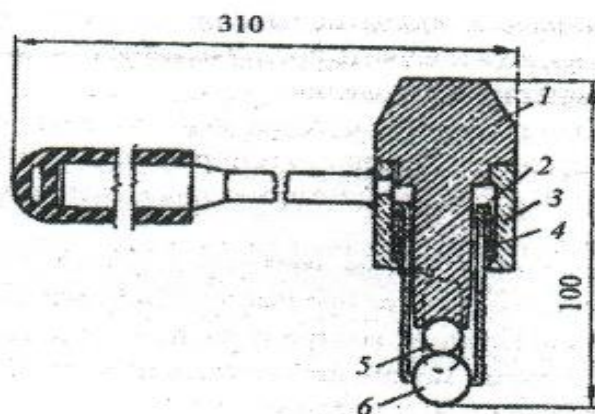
Молоток К.П.Кашкарова: 1 – головка; 2 – стакан; 3 – корпус; 4 – пружина; 5 – эталонный стальной стержень; 6 – шарик (индентор)
